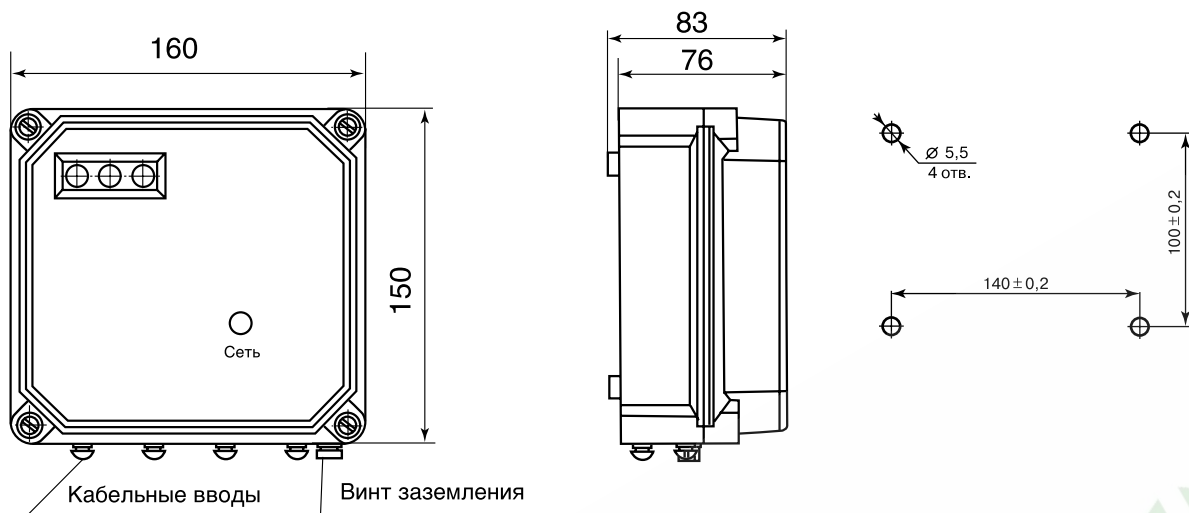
Габаритные и установочные размеры преобразователя передающего ППр
